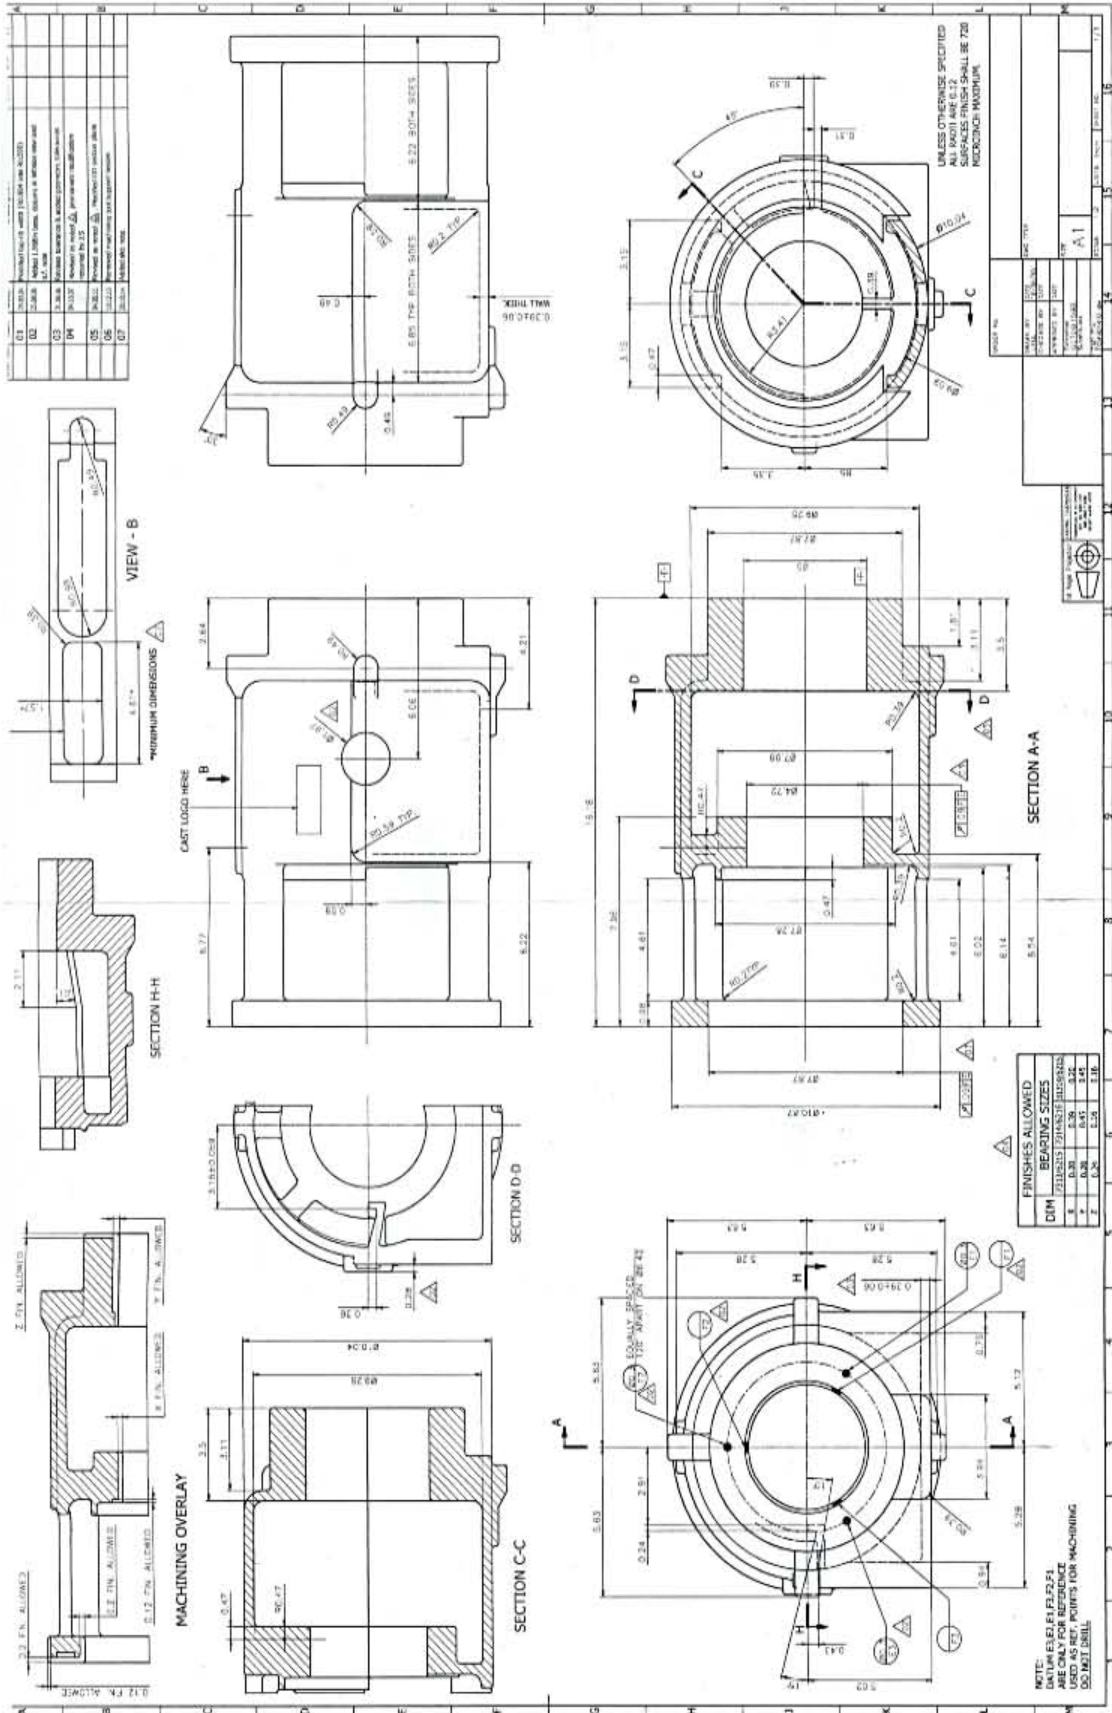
Plano 2D con todas las dimensiones del Bearing Housing.
